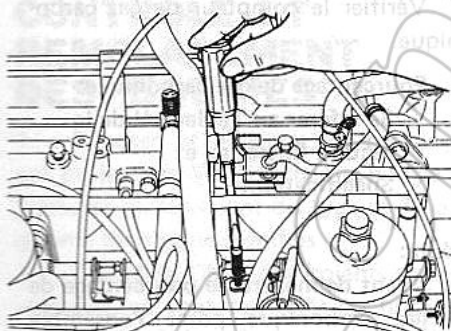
Desserrage de la vis de réglage d'équilibrage
